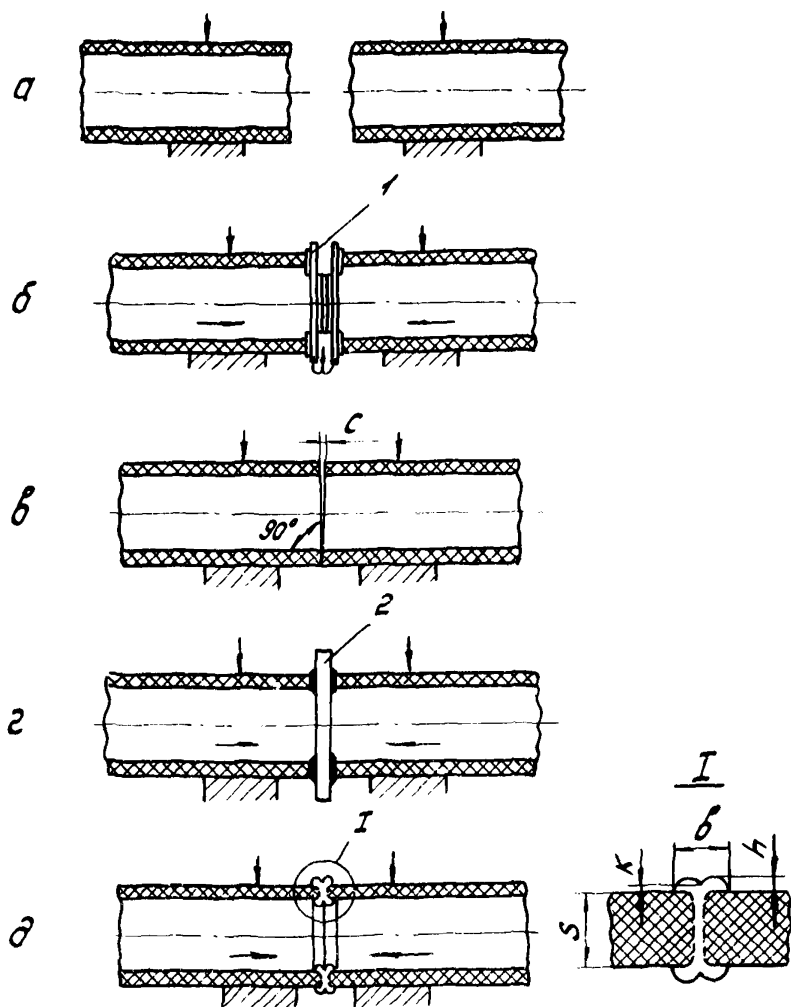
Последовательность процесса контактной сварки встык труб из полиэтилена:
